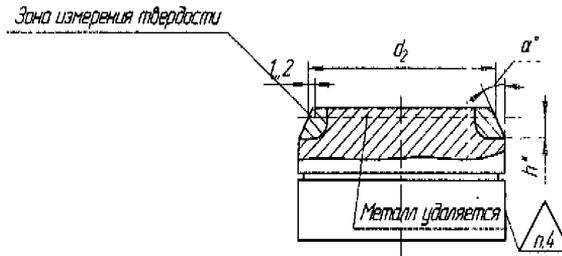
Образец для замера твердости деталей с конусным уплотнением
